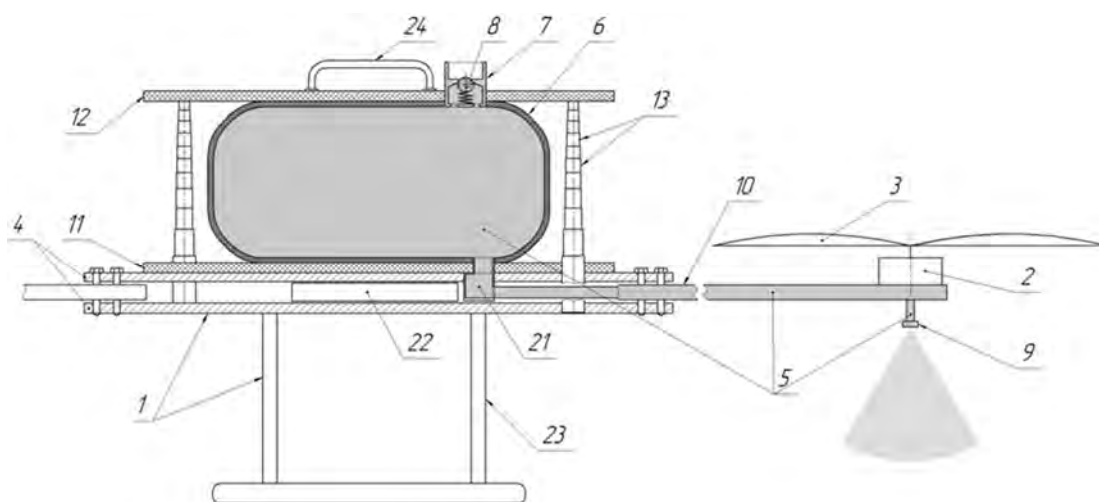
Беспилотный летающий опрыскиватель, вид сбоку
